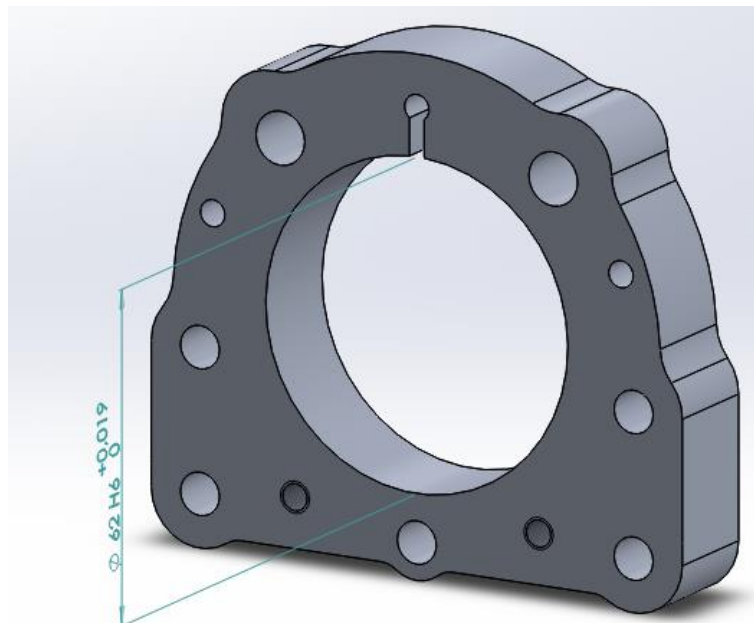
detalle tolerancia porta rodamientos. Fuente: propia.
